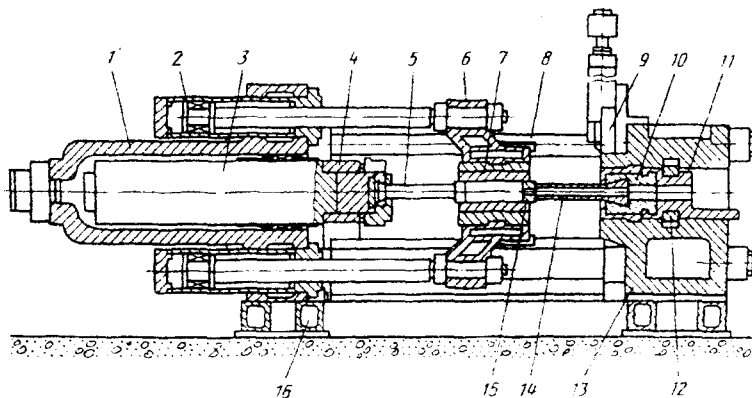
Прутково-профильный горизонтальный гидравлический пресс для прессования с прямым и обратным истечением металла: 1 - задняя поперечина - рабочий цилиндр; 2 - цилиндры передвижения контейнера; 3 - главный плунжер; 4 - прессующая траверса; 5 - пресс-штемпель; 6 - контейнеродержатель; 7 - контейнер; 8 - колонна; 9 - ножницы для отделения пресс-остатка; 10 - салазки; 11 - мундштук шплинтон; 12 - затвор мундштука; 13 - передняя поперечина; 14 - шплинтон; 15 - матрица; 16 - станина
